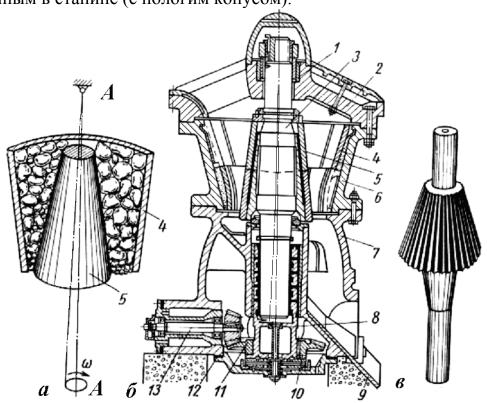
Конусная дробилка с крутым конусом: a – схема работы; δ – разрез; ϵ – конструкция главного вала с дробящим конусом
